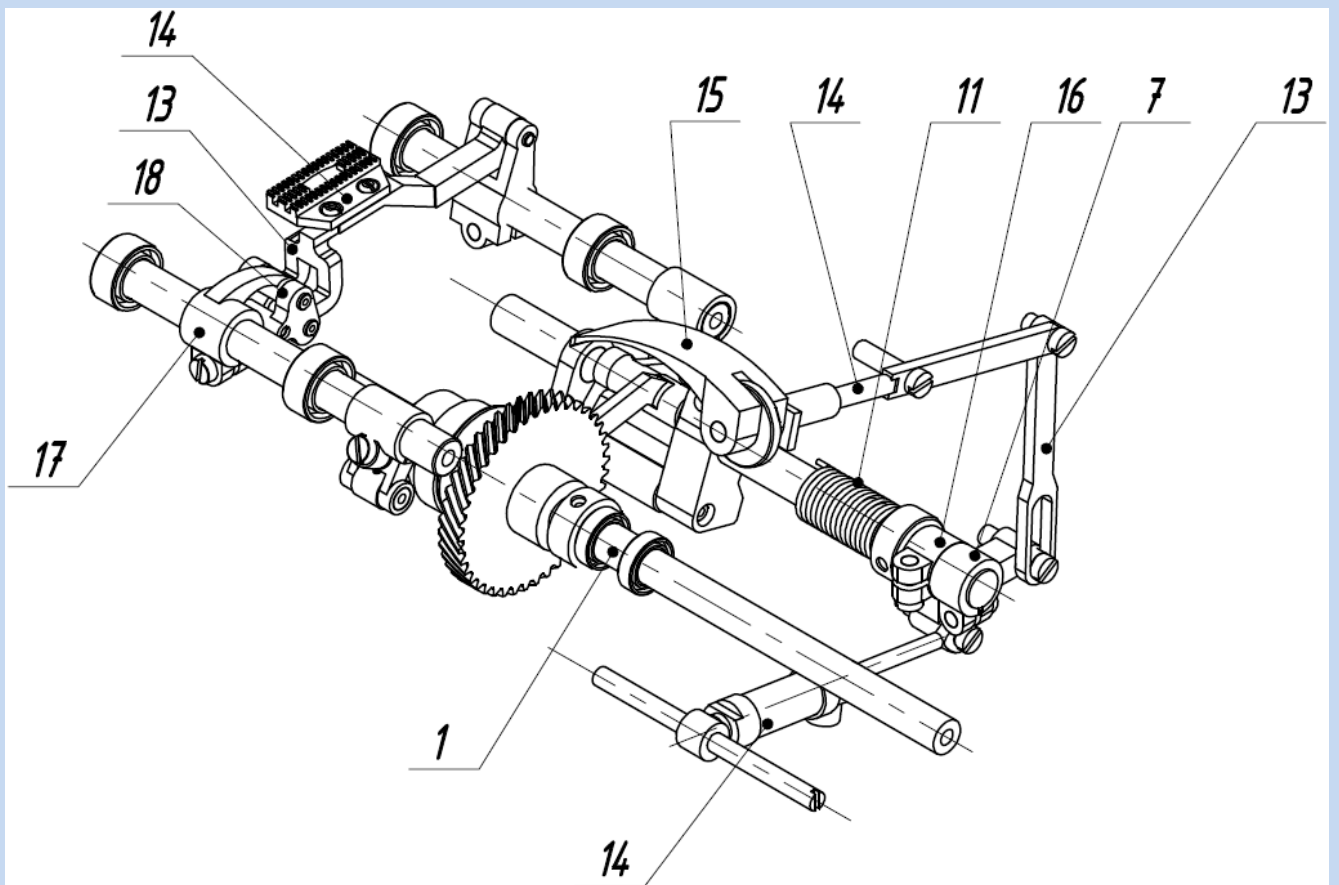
Конструктивна схема механізму зубчастої рейки
